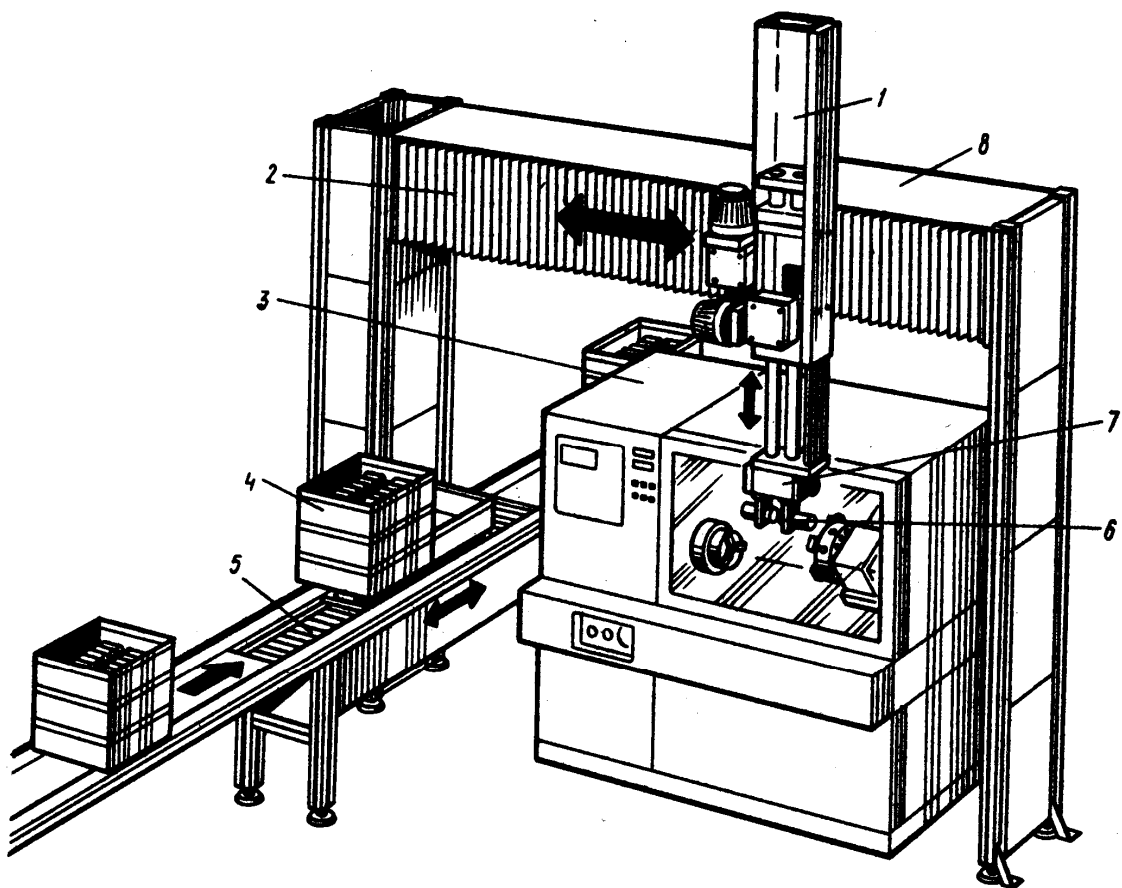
Обслуговування токарного верстата роботом порталного типу:
